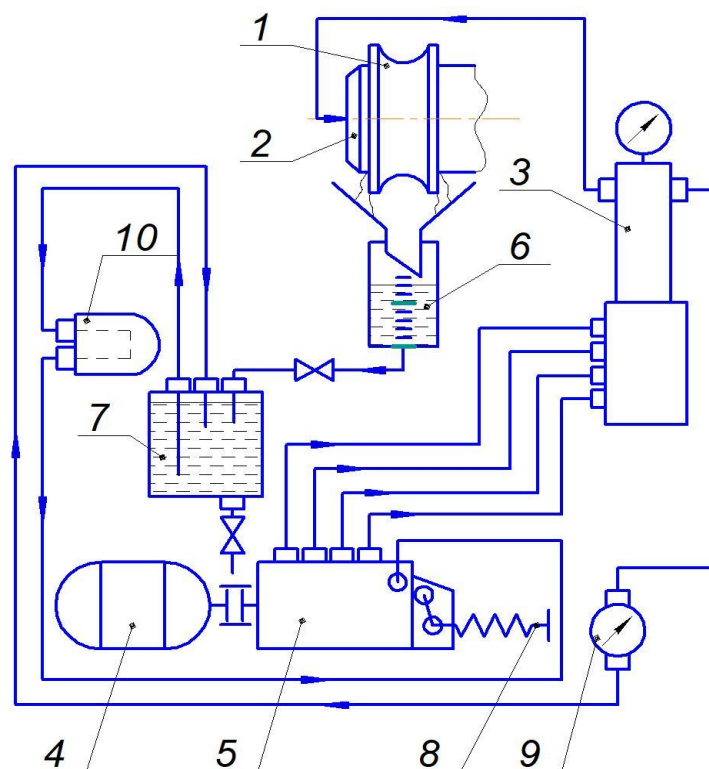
Принципиальная схема устройства для осуществления способа безразборной оценки неподвижного соединения с натягом: 1 – кольцо подшипника качения; 2 – вал; 3 – гаситель пульсации; 4 – привод насоса; 5 – насос высокого давления; 6 – мерный стакан; 7 – емкость; 8 – регулятор давления; 9 – грубый регулятор давления; 10 – фильтр.
